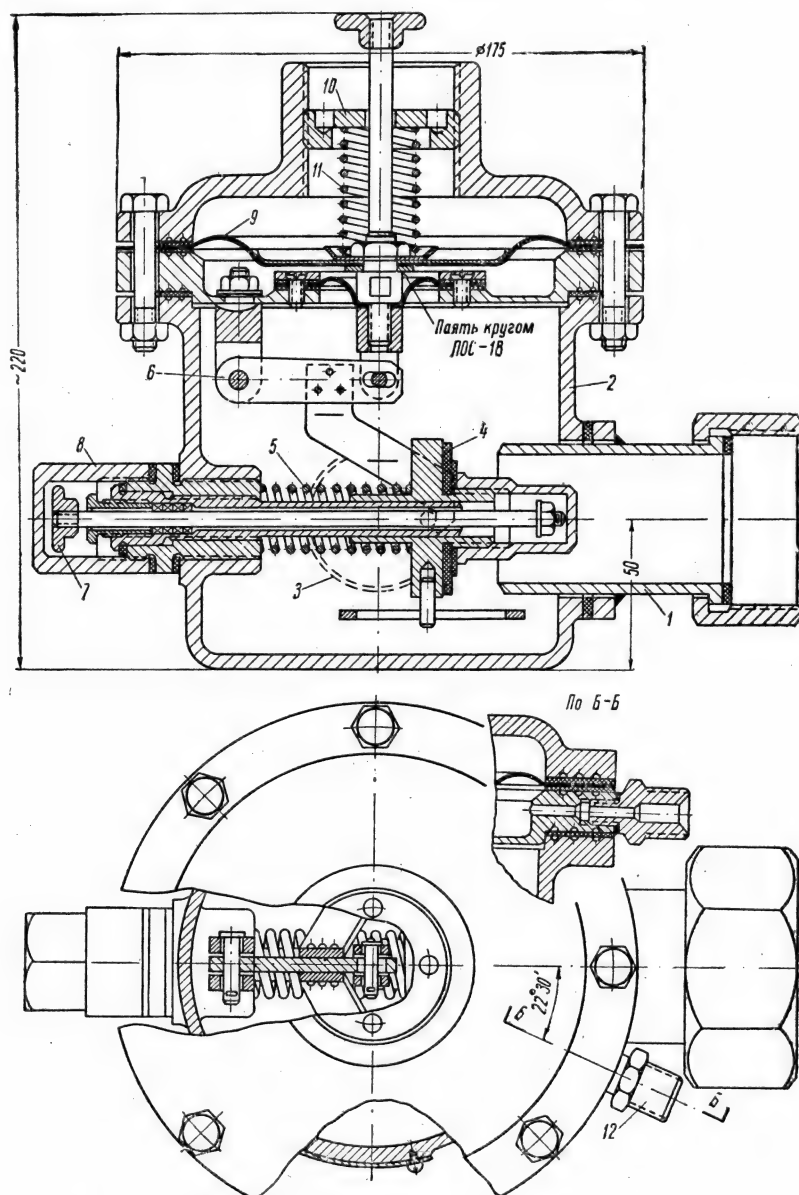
Предохранительный запорный клапан типа ПЗК_Н-50:
